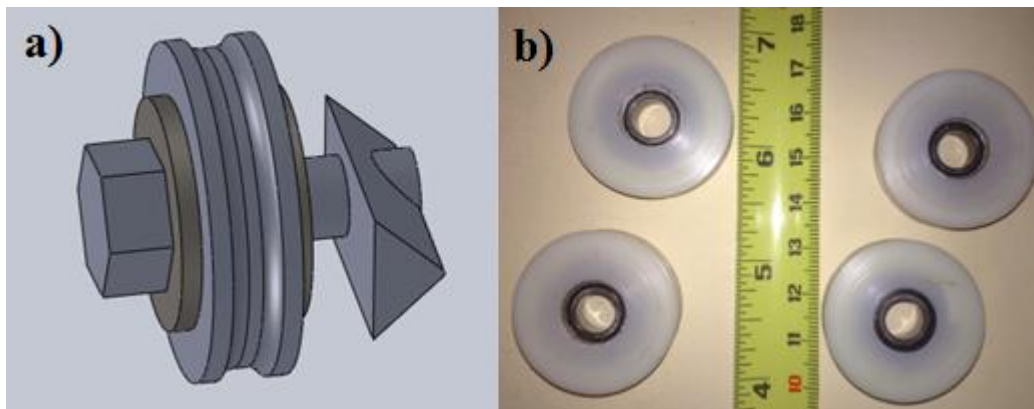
a) vista del ensamble de una polea, tornillo y tuerca. b) Poleas con rodamiento para transmitir la carga
